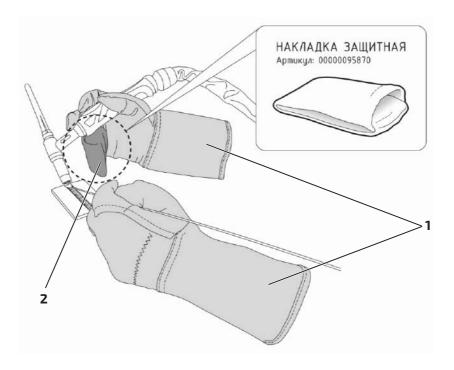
Перчатки и накладка защитная для TIG сварки.
